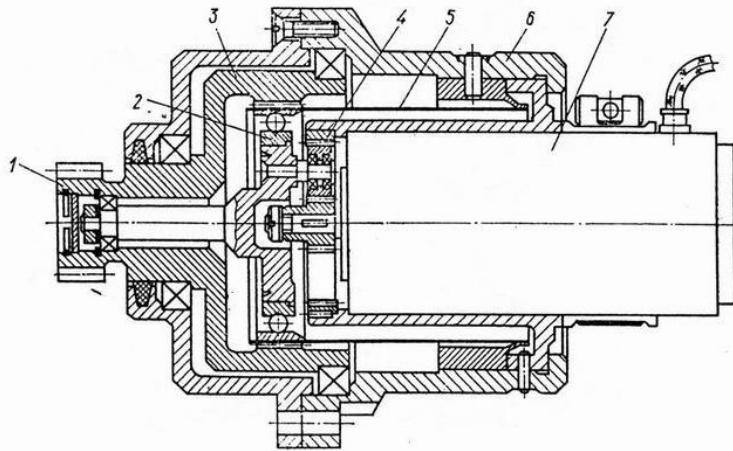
Конструкція мотор-редуктора з хвильовою та планетарною передачами
